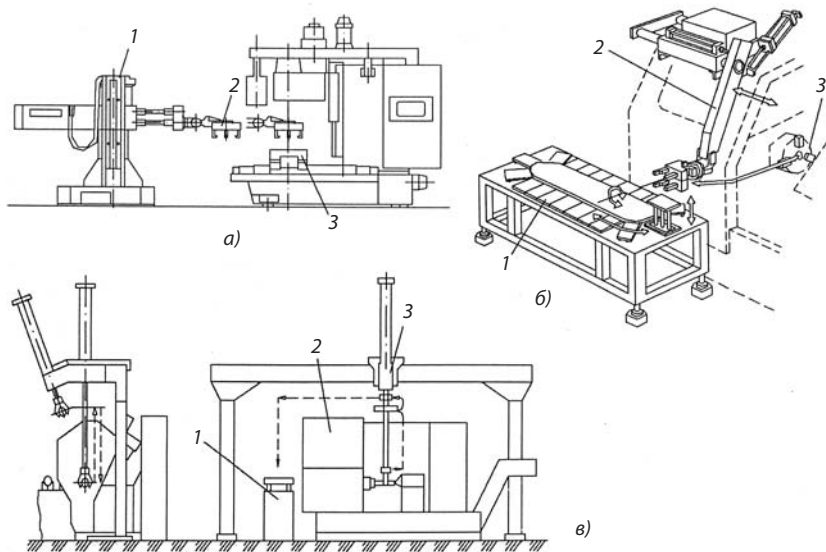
Схемы автоматизации загрузки-разгрузки заготовок и деталей на станках с ЧПУ:
